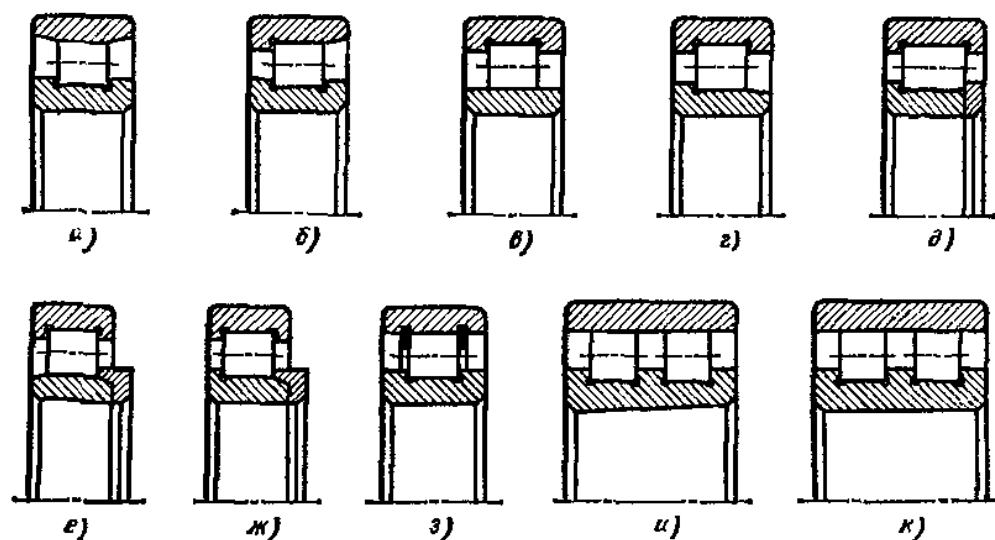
Роликподшипники с короткими цилиндрическими роликами типов:
